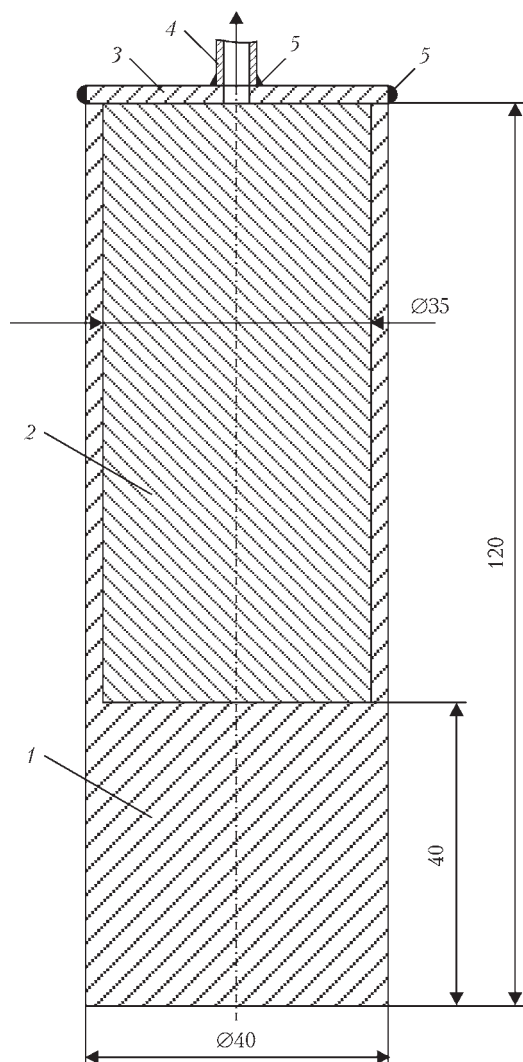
Эскиз опытной заготовки для пайки: 1 — полый цилиндр; 2 — расплавляемый компонент (медь); 3 — крышка; 4 — патрубок для вакуумирования; 5 — герметизирующие сварные швы
